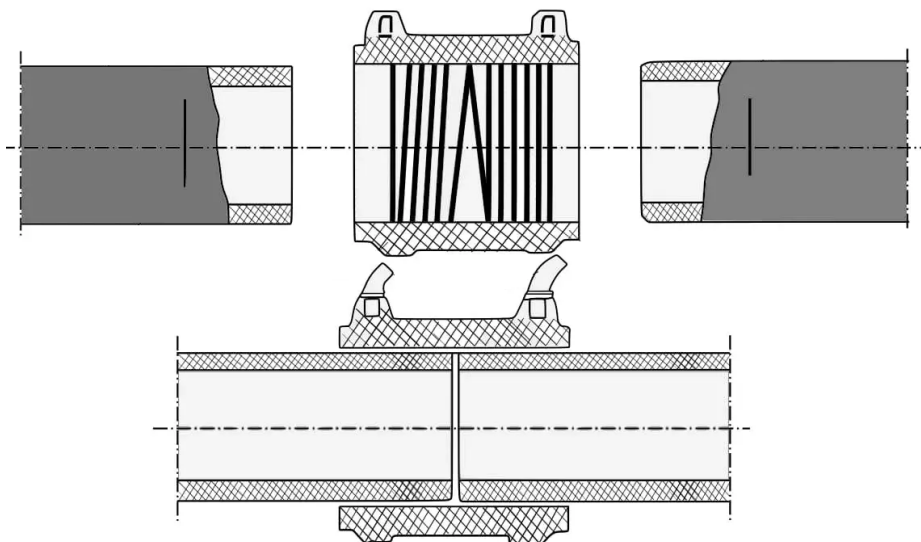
Муфтовая сварка пластмассовых труб
